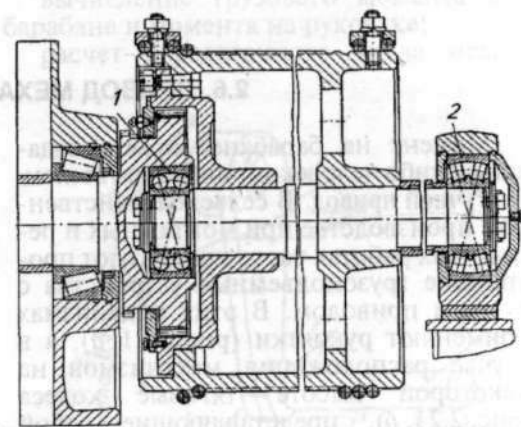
Конструкция барабана, одна из опор которого установлена внутри выходного вала редуктора
